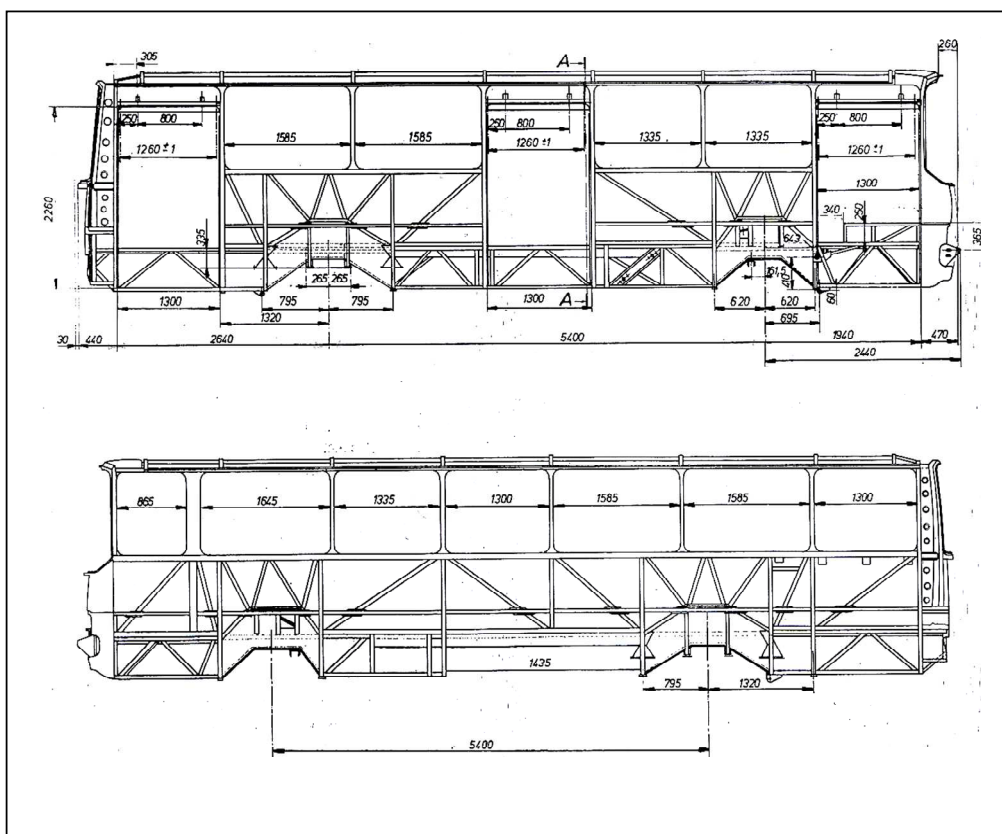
Сборочный чертеж боковин каркаса автобуса
